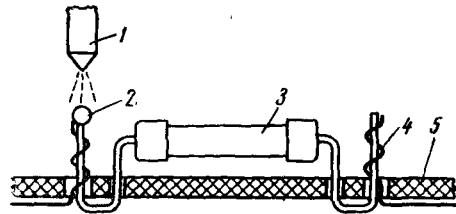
Схема радиомонтажной сварки угольным карандашом:
